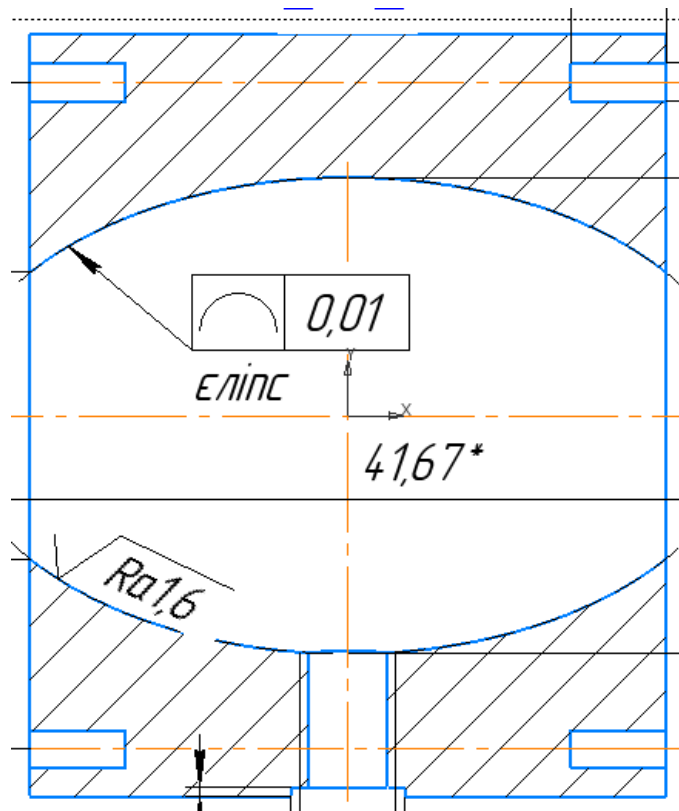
Ескіз деталі «оптичний дефлектор»
